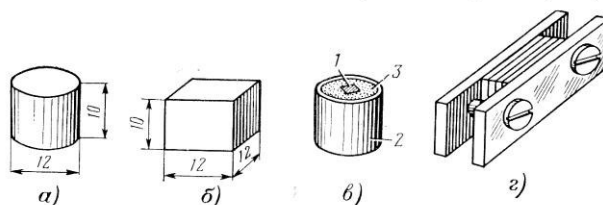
Нормальные размеры металлографических образцов (а и б) и приспособления для приготовления микрошлифов (в и г):
